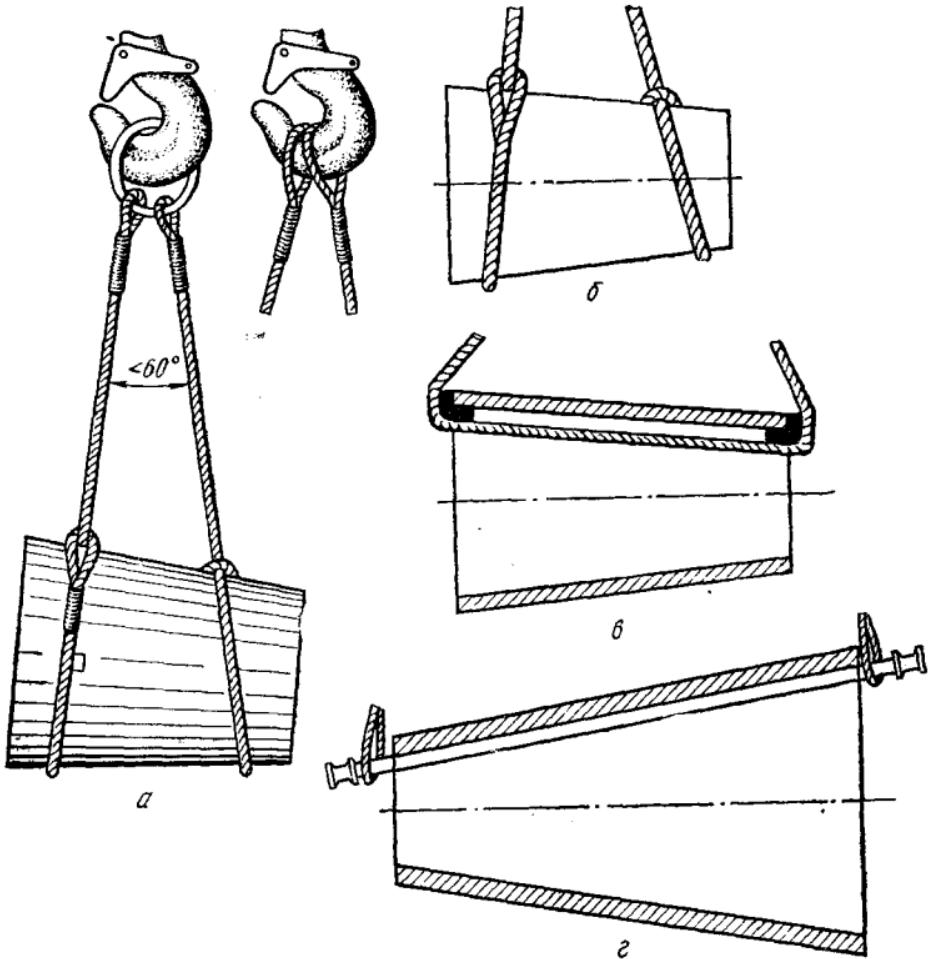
Строповка деталей типа конуса для транспортирования в горизонтальном положении:
